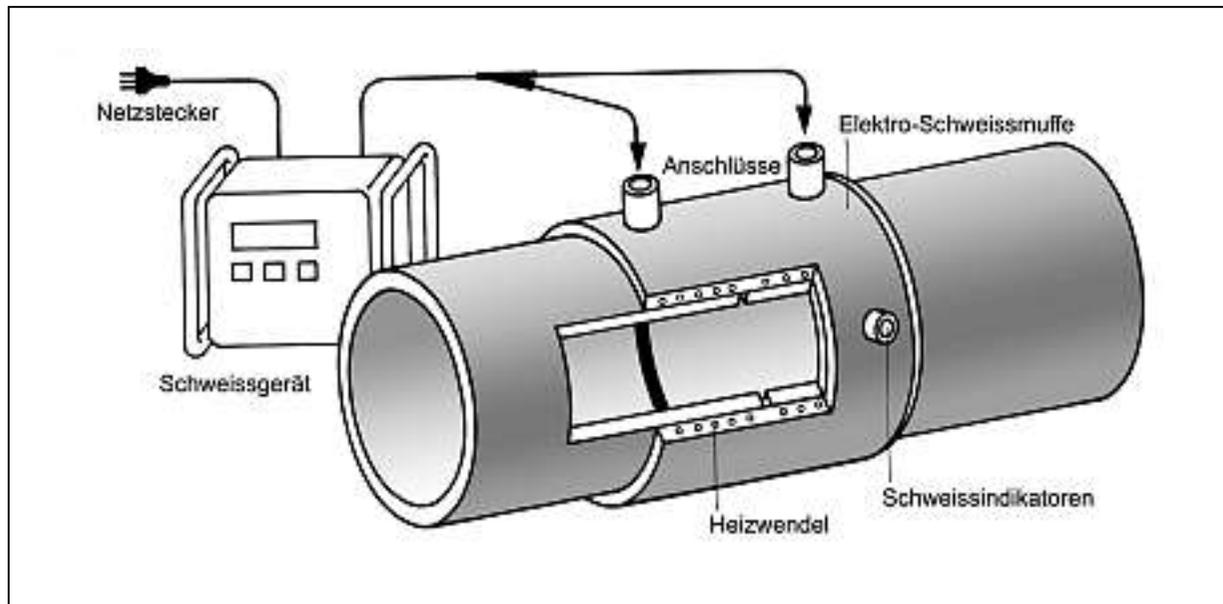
Prinzip der Elektro-Schweißung am Beispiel einer Verbindung mit einer Elektro-Schweissmuffe
